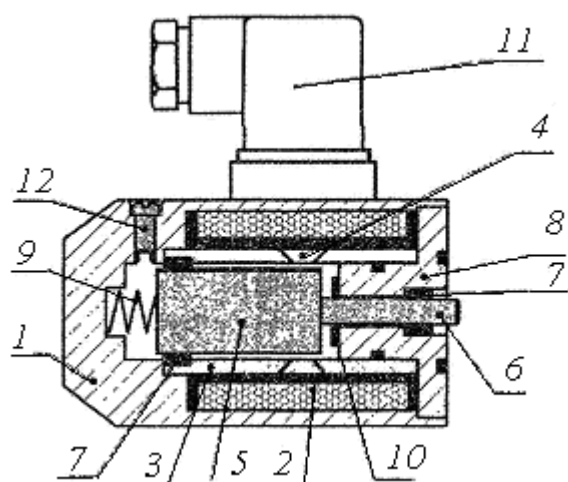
Конструкція пропорційного електромагніту: 1 – корпус; 2 – обмотка; 3 – циліндровий магніт; 4 – керуючий конус; 5 – якор; 6 – направляючий стрижень; 7 – підшипники ковзання; 8 – внутрішній магніт; 9 – пружина; 10 – стопорний диск; 11 – електричне рознімання; 12 – гвинт
